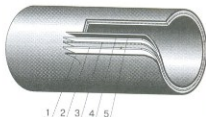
Конструкция металлополимерной трубы: 1, 5 — полиэтилен; 2, 4 — клеювая композиция; 3 — фольга
